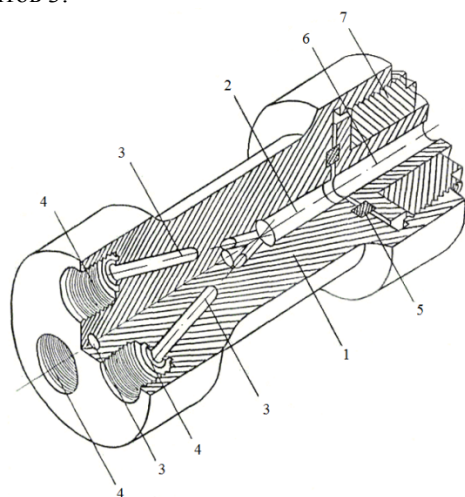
Конструкция формующей головки для изготовления слойно-секторных полимерных изделий: 1 - корпус формующей головки; 2 - соединительный канал; 3 - подводный канал; 4 - гнезда для подсоединения цилиндра высокого давления; 5 - уплотнительное кольцо; 6 - формующий канал; 7 - прижимная гайка
